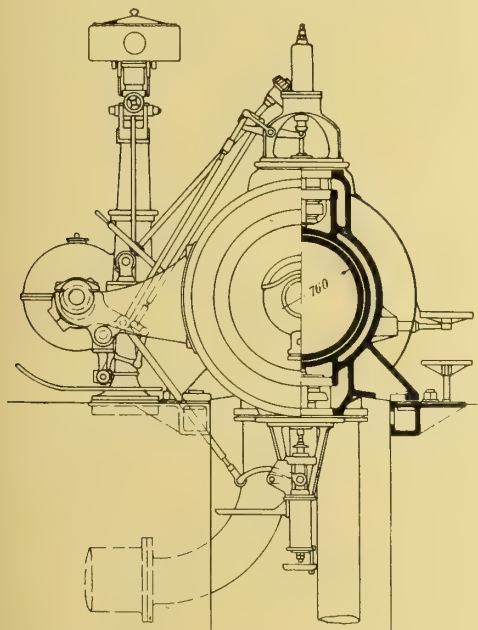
Verbunddampfmaschine der Zeche „Victor“. Steuerungseinrichtung des Hochdruckzylinders.
